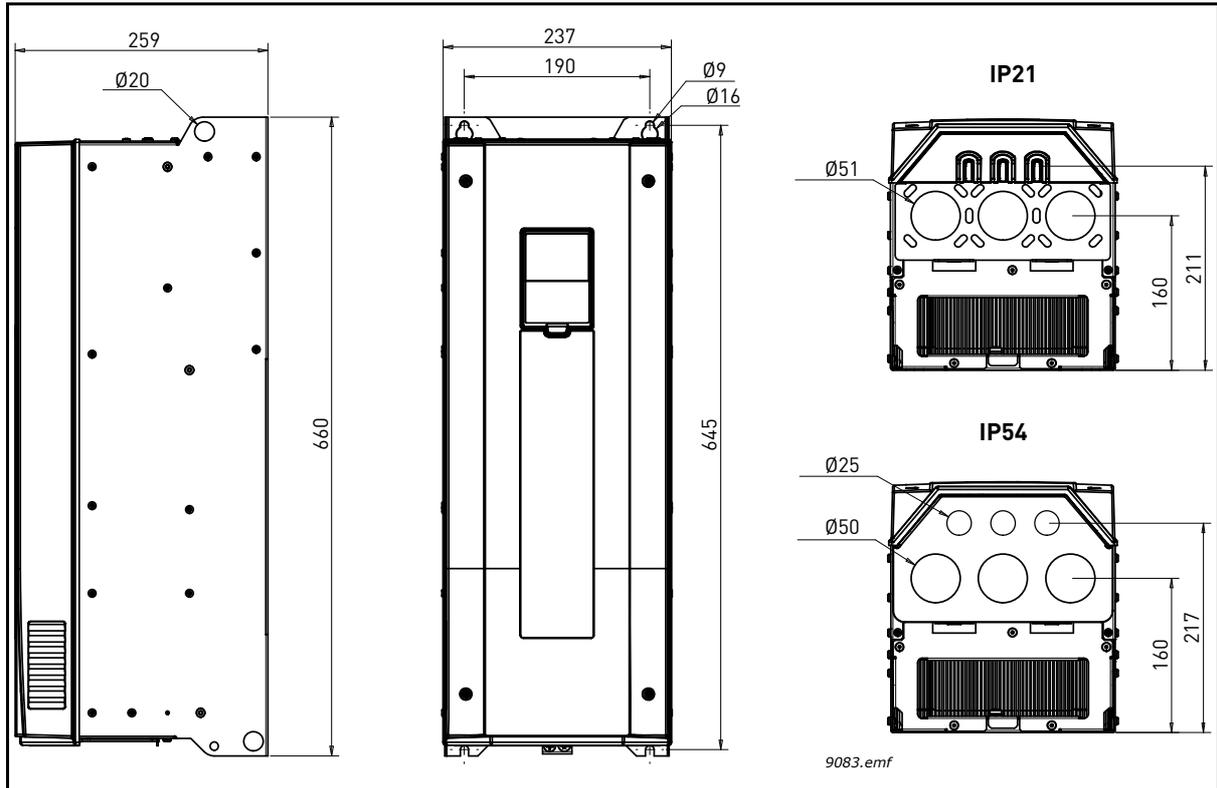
Dimensiones del variador de CA Vacon, MR7, montaje para la pared
